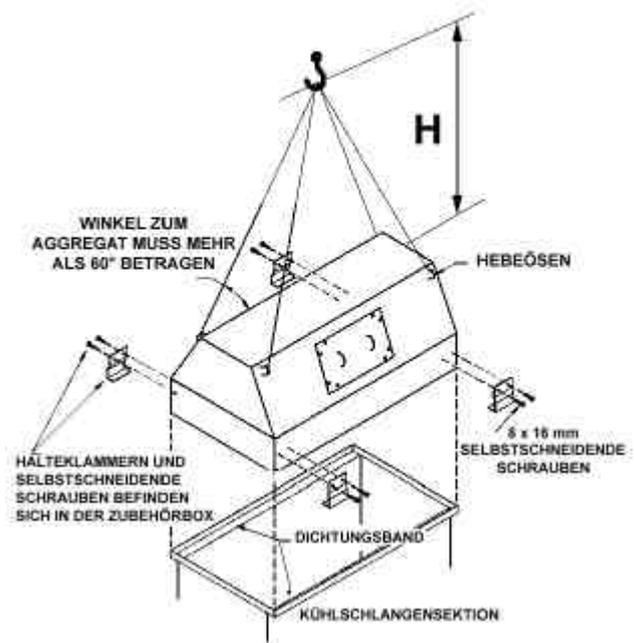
Verschrauben der Ausblashaube bzw. des Schalldämpfers mit dem Oberteil
